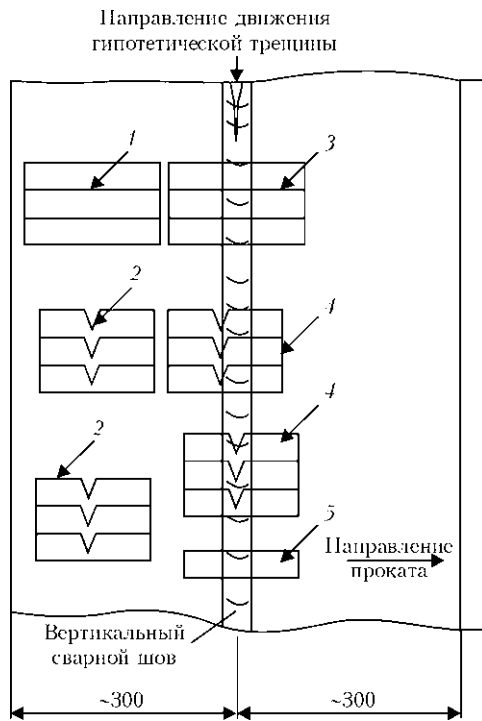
Схема вырезки образцов из сварного стыка: 1, 3 — образцы для прочностных испытаний соответственно основного металла и сварного соединения; 2, 4 — образцы для определения ударной вязкости основного металла, а также металла шва и ЗТВ с круглым (KCU) и острым (KCV) надрезами; 5 — образцы для металлографических исследований
